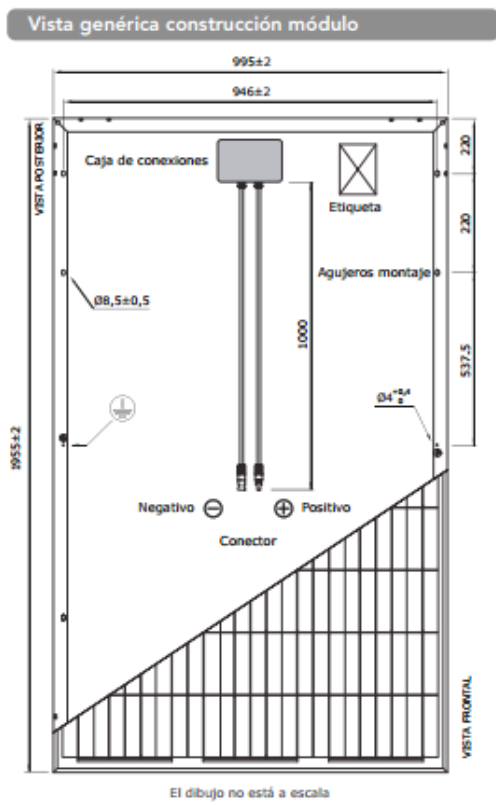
Plano acotado de modulo fotovoltaico A-310
